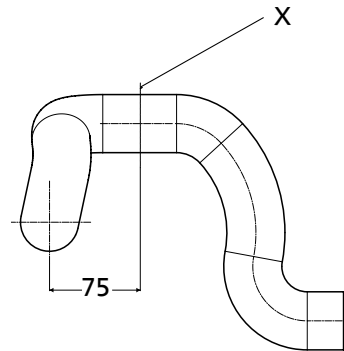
Druckschlauch bei Druckabgang rechts, Abmessung [mm]
